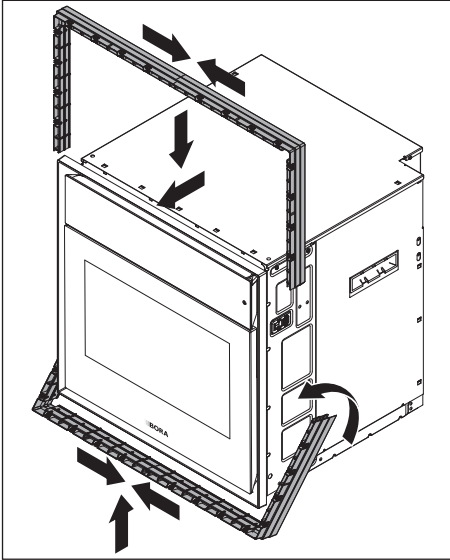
Montagem de 2 estruturas de espaçamento
